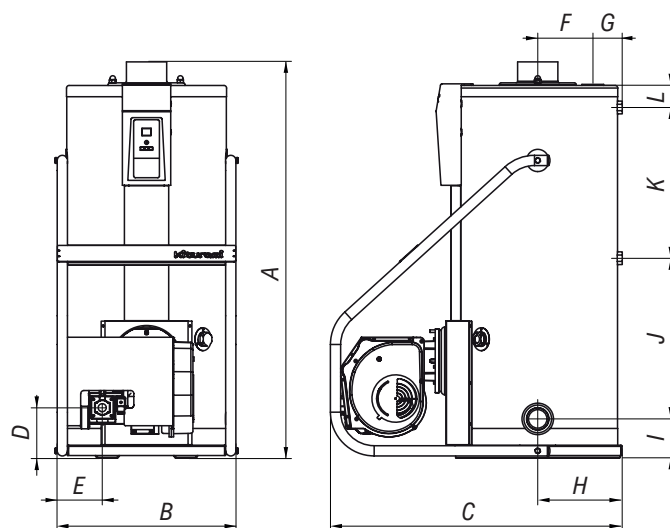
Габаритные размеры KSG HiFin 116/174
